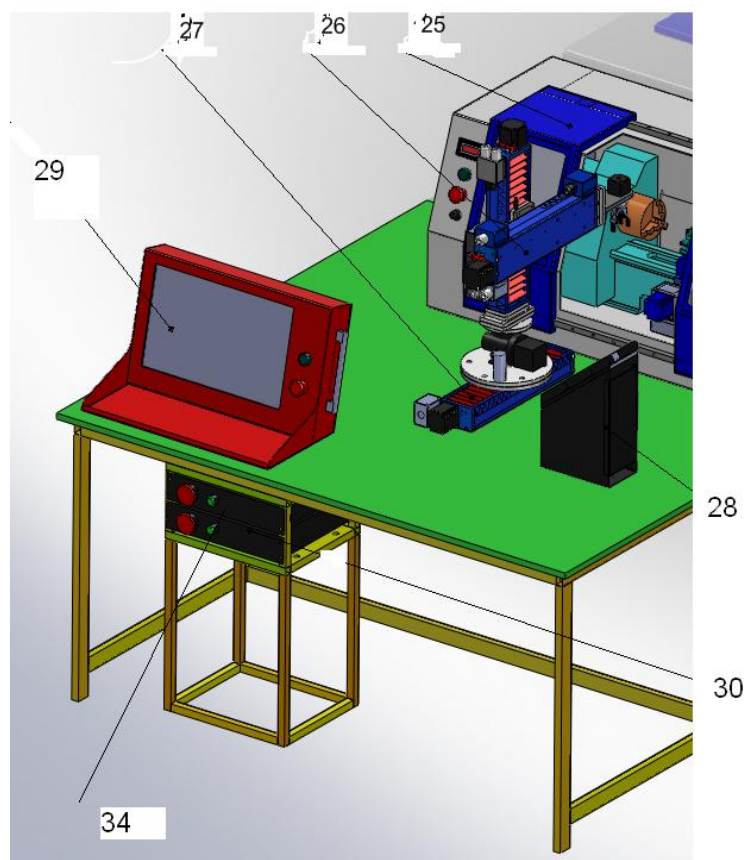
Модель ГПМ на базе токарного станка с компьютерным управлением
